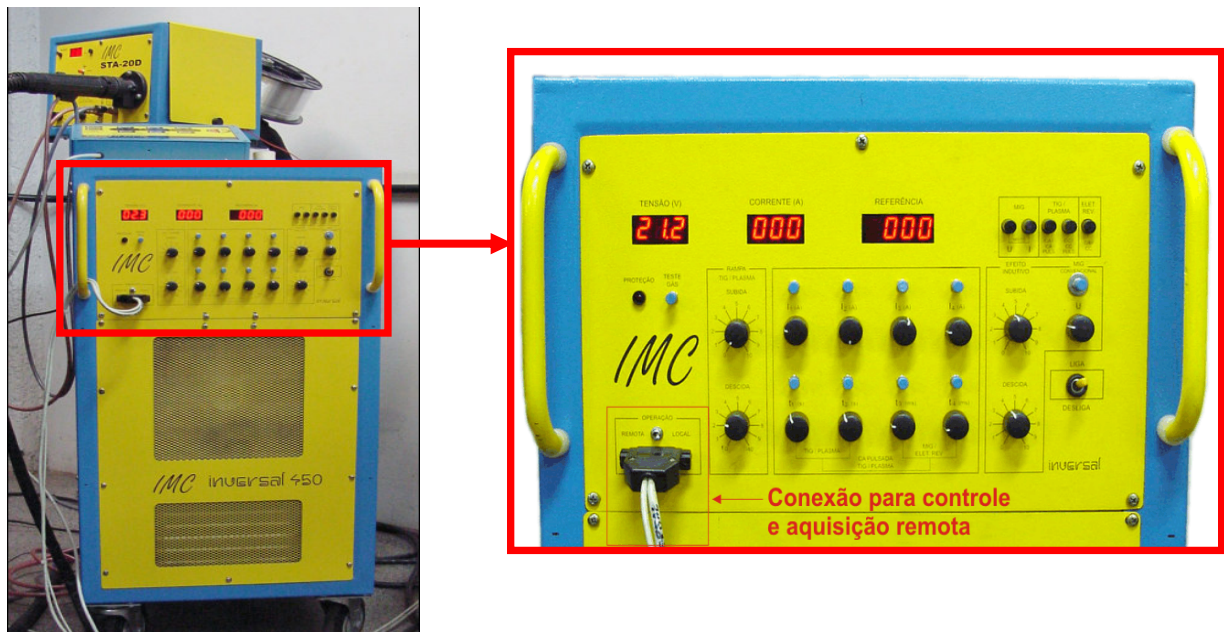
Fonte de Soldagem Inversal 450/IMC.
